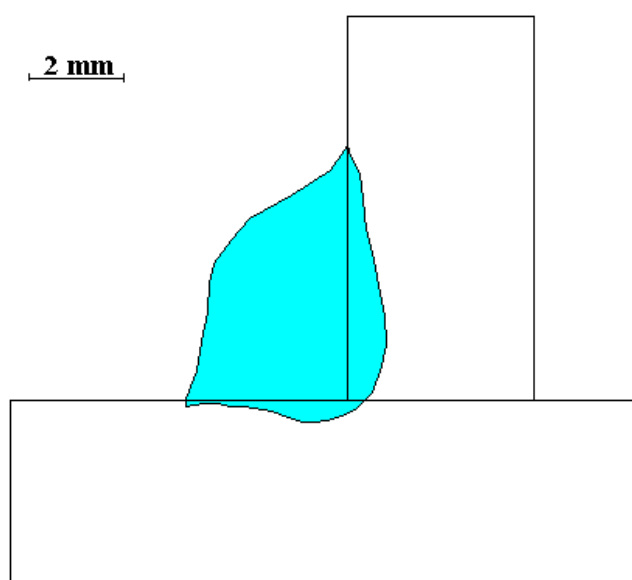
Geometrie makrostruktury vzorku X4c025
